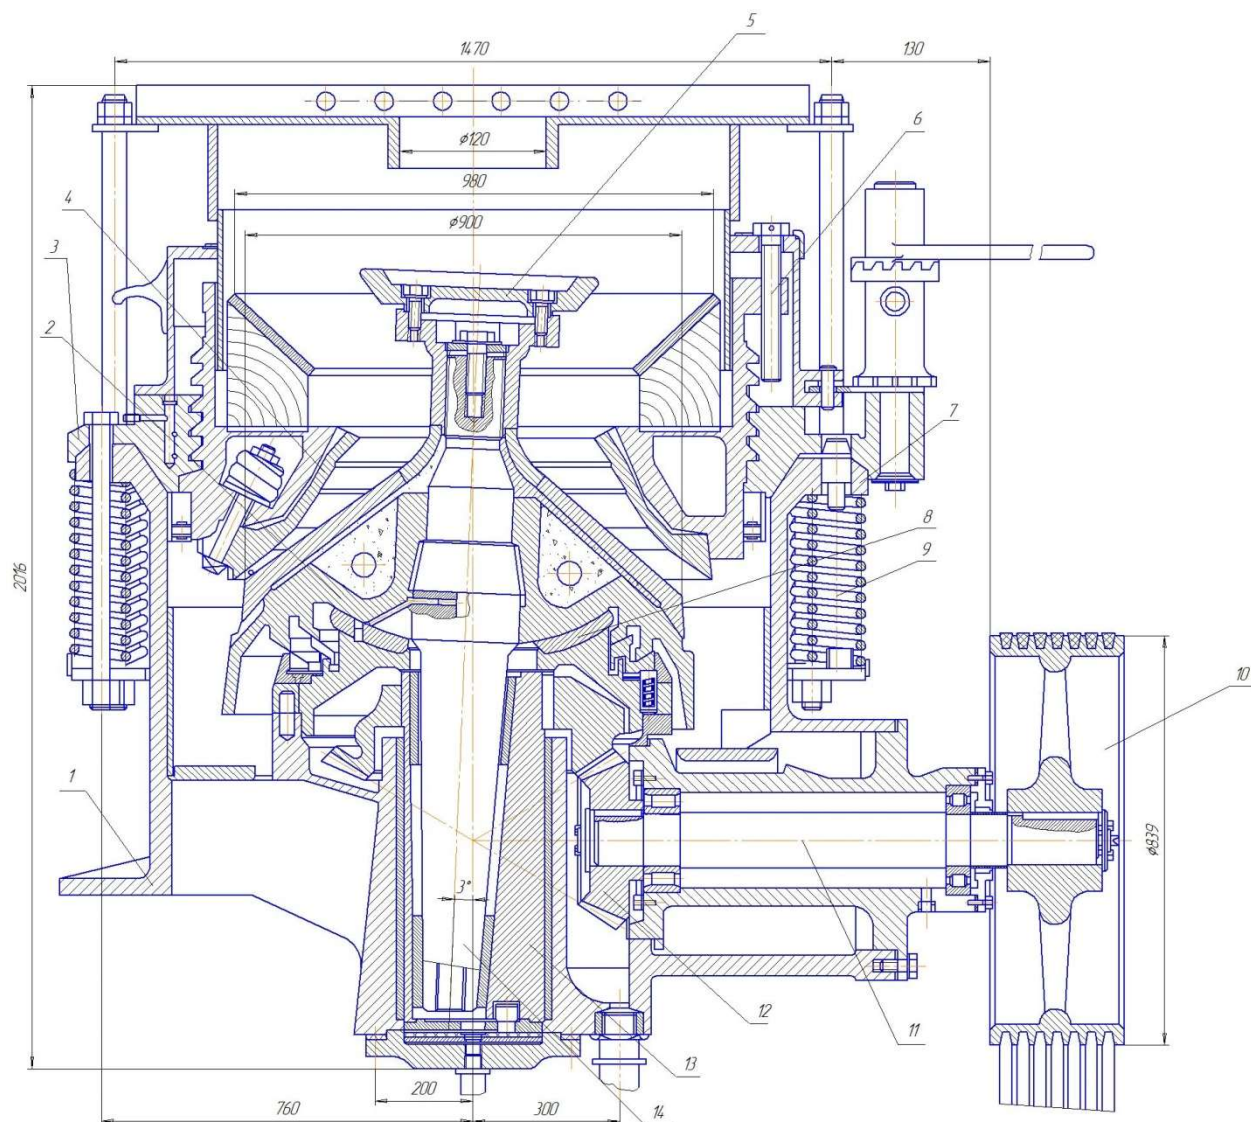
Дробарка конусна КМД 2200: 1 – станина; 2 – рухомий конус; 3 – установче кільце; 4 – конус нерухомий; 5 – розподільча тарілка; 6 – палець; 7 – фланець станини; 8 – підп’ятник; 9 – пружина; 10 – шків привідний; 11 – вал приводу; 12 – шестерня конусна; 13 – втулка ексцентрику; 14 – вал рухомого конусу
